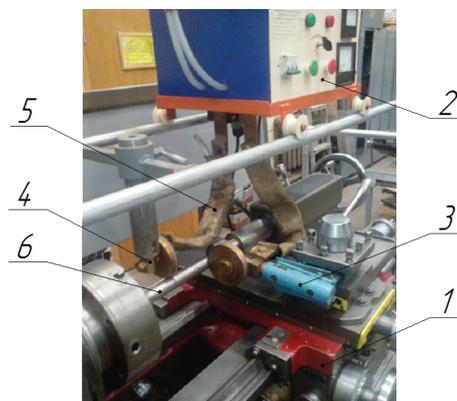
Фрагмент размещения оборудования и процесса ЭМПЗ образцов на токарно-винторезном станке 16К20:
